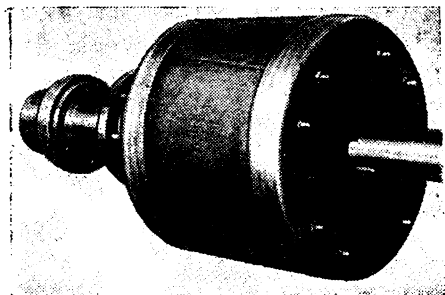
Барабан с резиновой диафрагмой для сборки шин типа Р.
